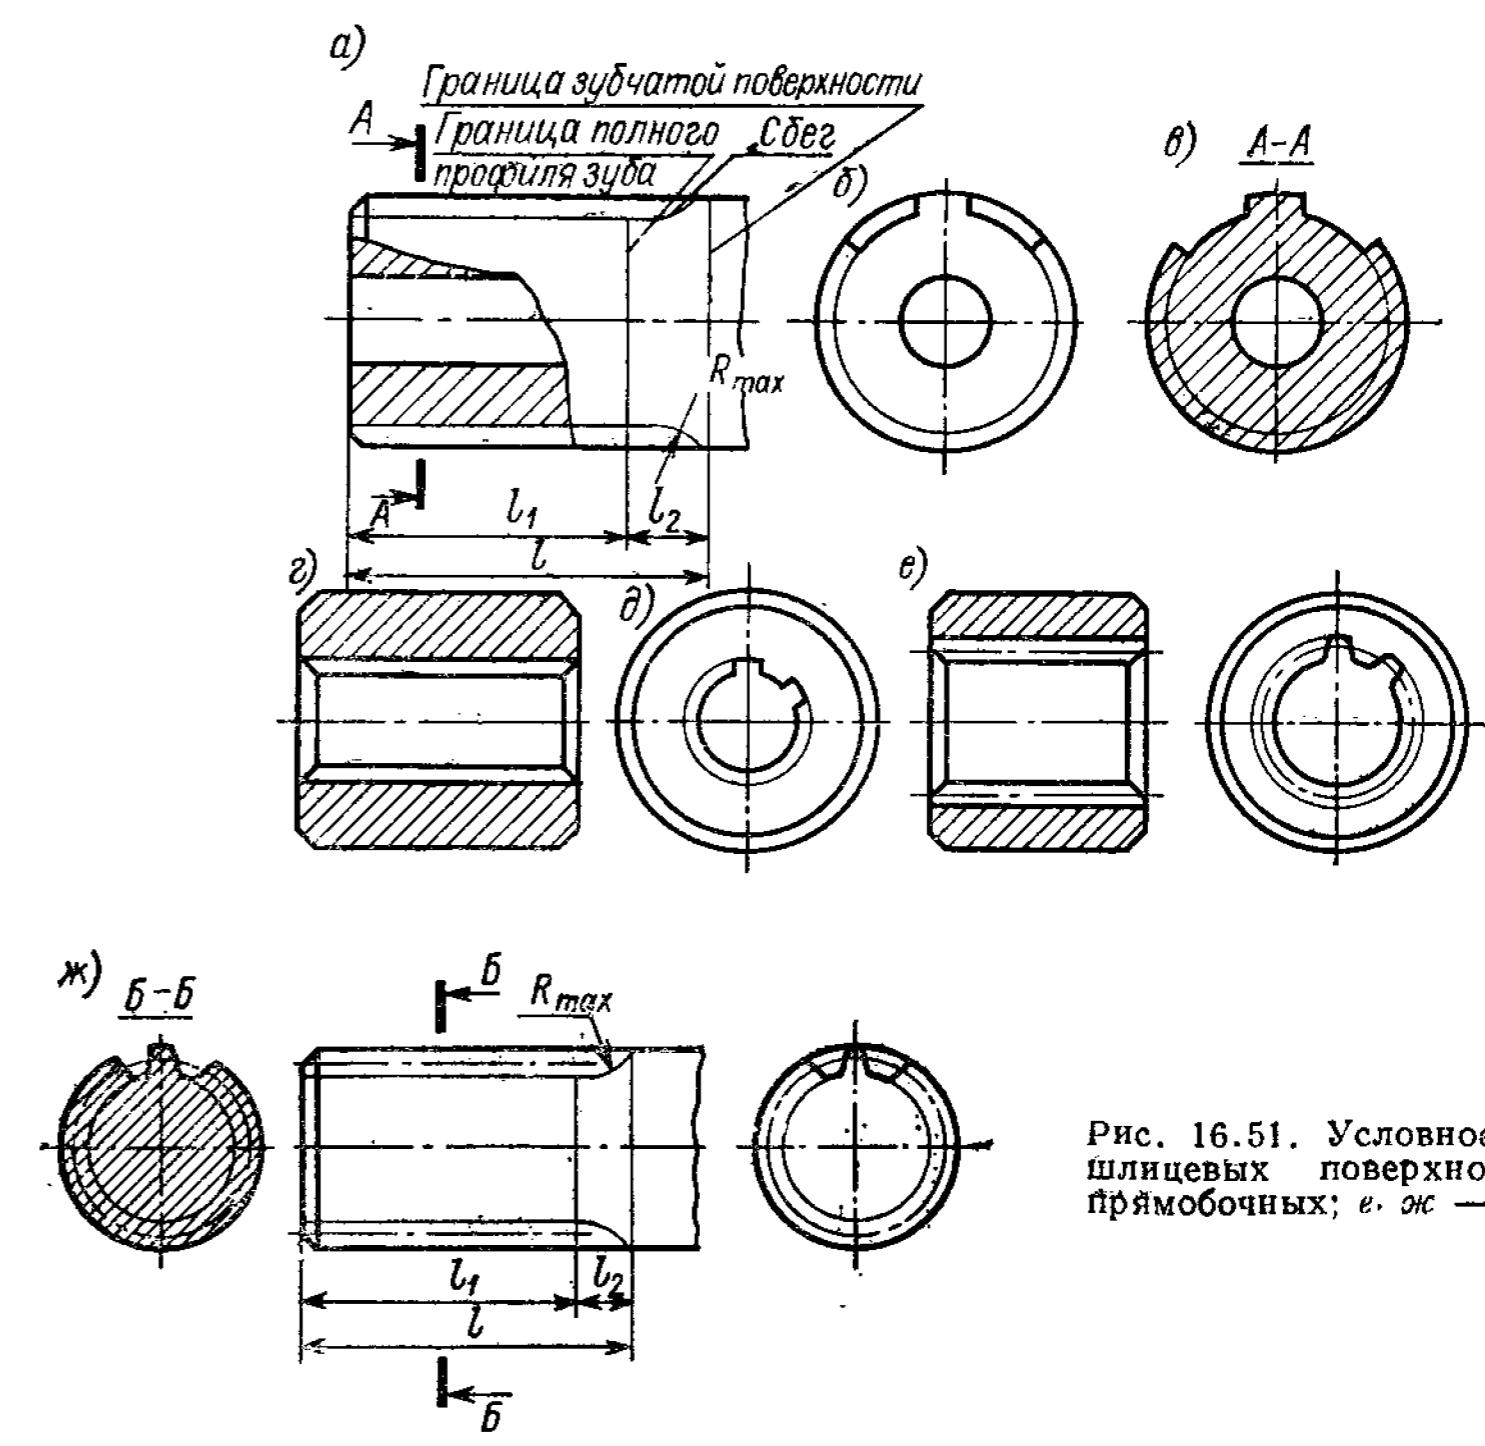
Условное изображение шлицевых поверхностей: а—д — прямобочных; е, ж — эвольвентных
